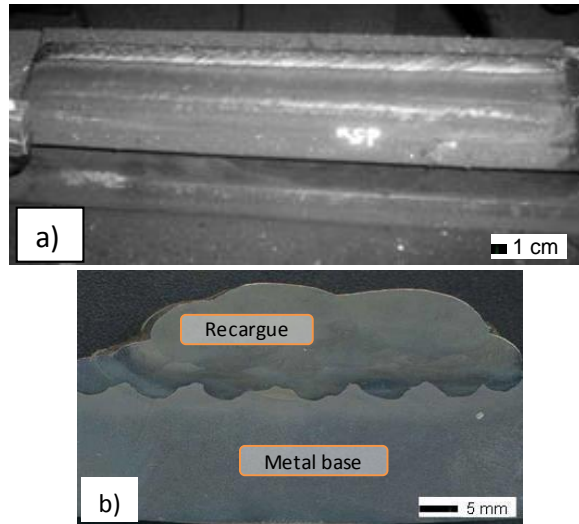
a) Probeta soldada, b) Corte transversal de la probeta soldada.
